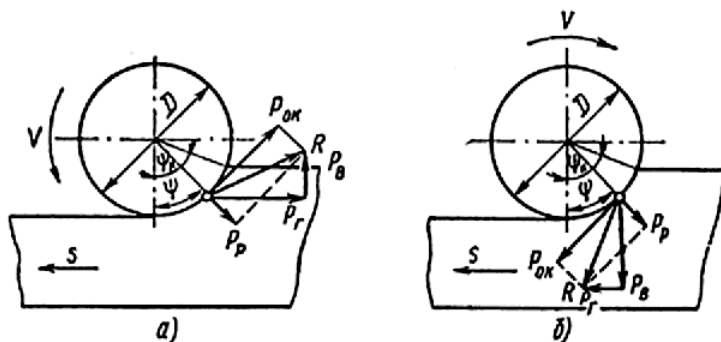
Схемы действия сил при фрезеровании цилиндрической фрезой:
